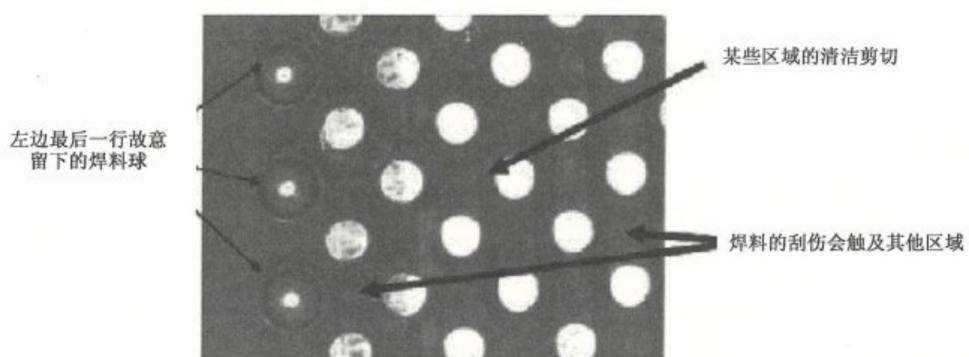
采用球剪切程序的 BGA 焊锡球去除
